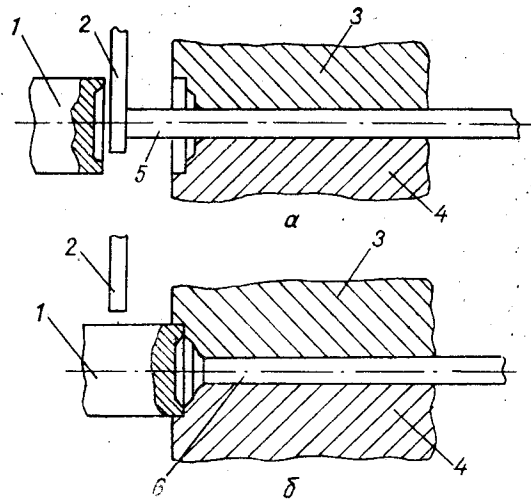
Стадії виготовлення (а, б) заготовок клапанів на ГKM:
